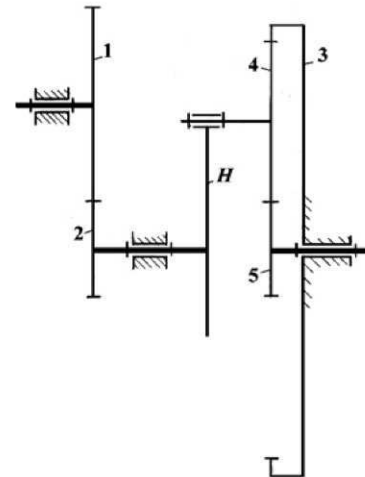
Двухступенчатый зубчатый механизм
